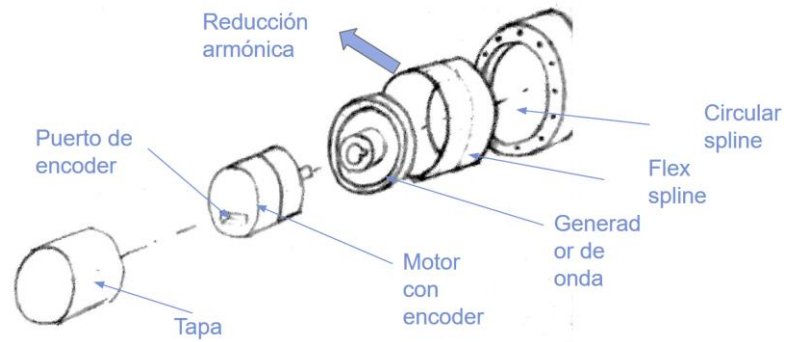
Vista explosionada posterior de Cilindro Rotacional
